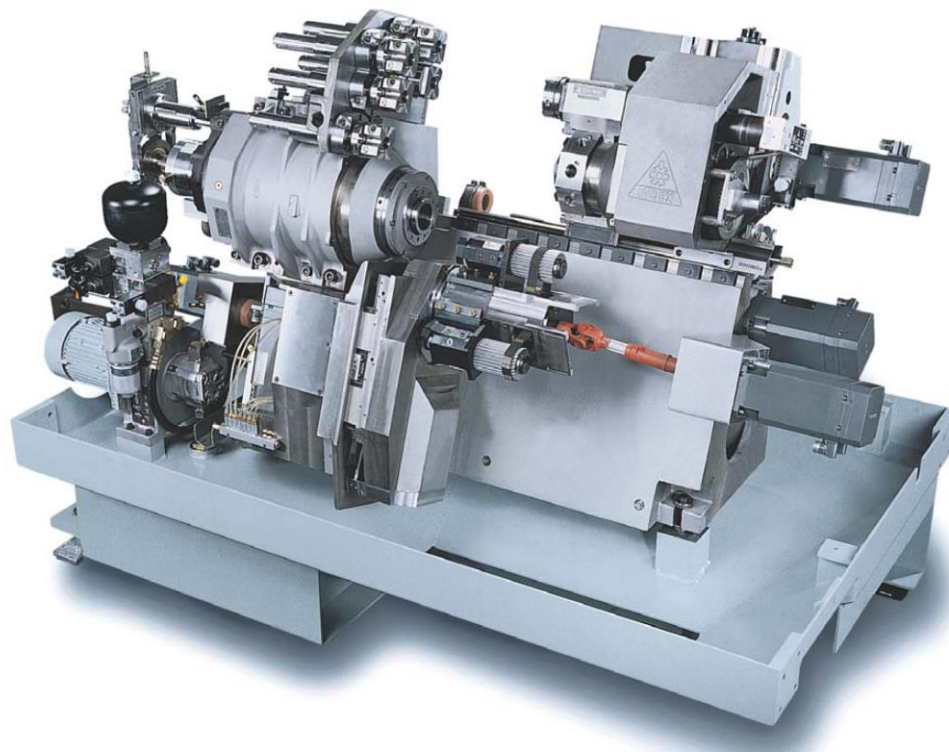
Верстат токарно-револьверний ABC 42 з ЧПУ фірми Index Werke
